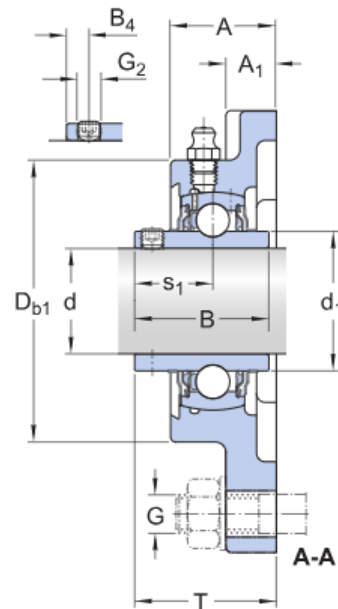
Зображення корпусного самоцентрівного підшипника UCF207 [5]
